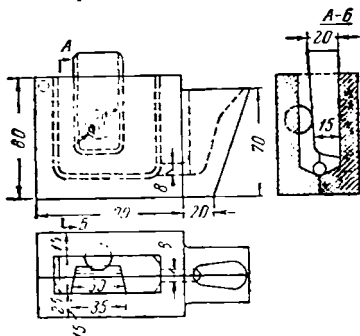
Металлическая форма для отливки шариковой пробы А. Г. Спасского
